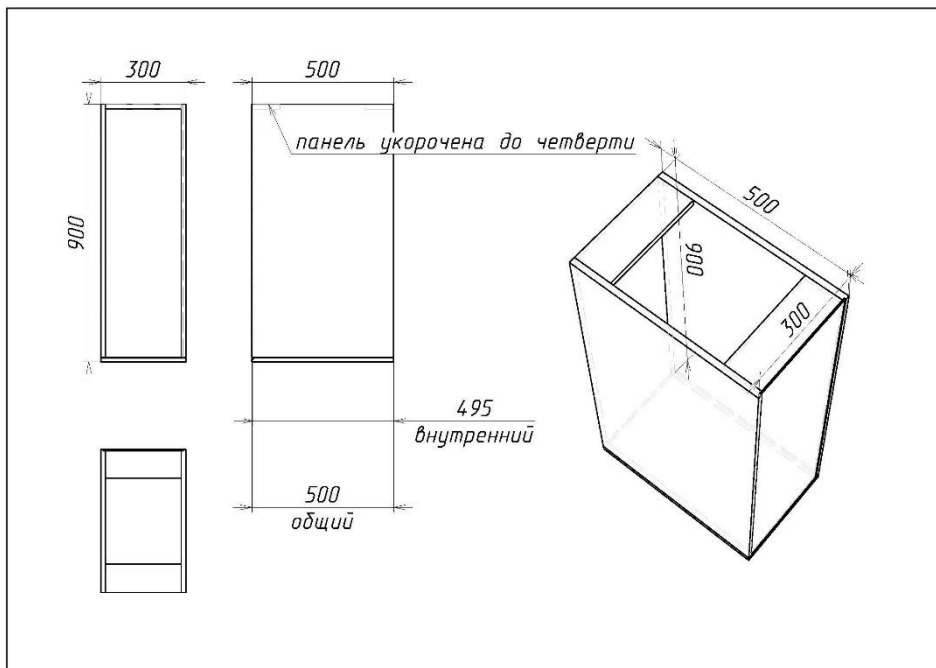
Установка задней стенки в четверть в корпус с вкладными крышкой и дном (БМ)
